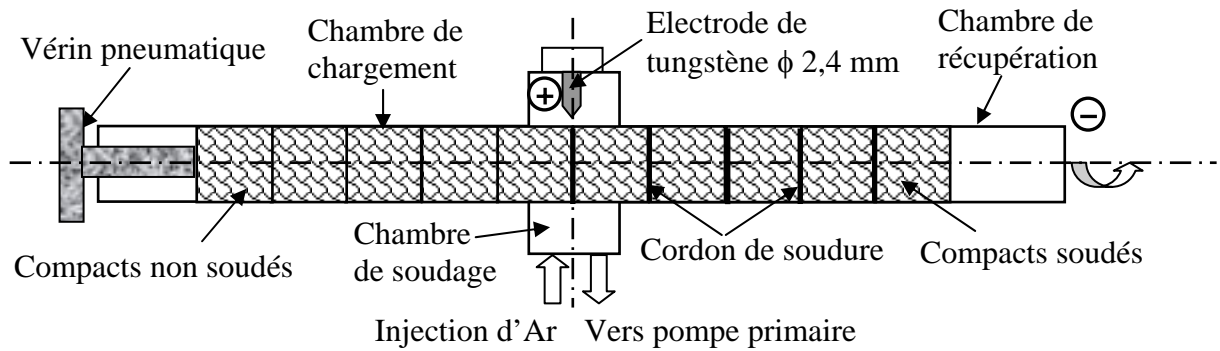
schéma synoptique du dispositif de soudage radial
